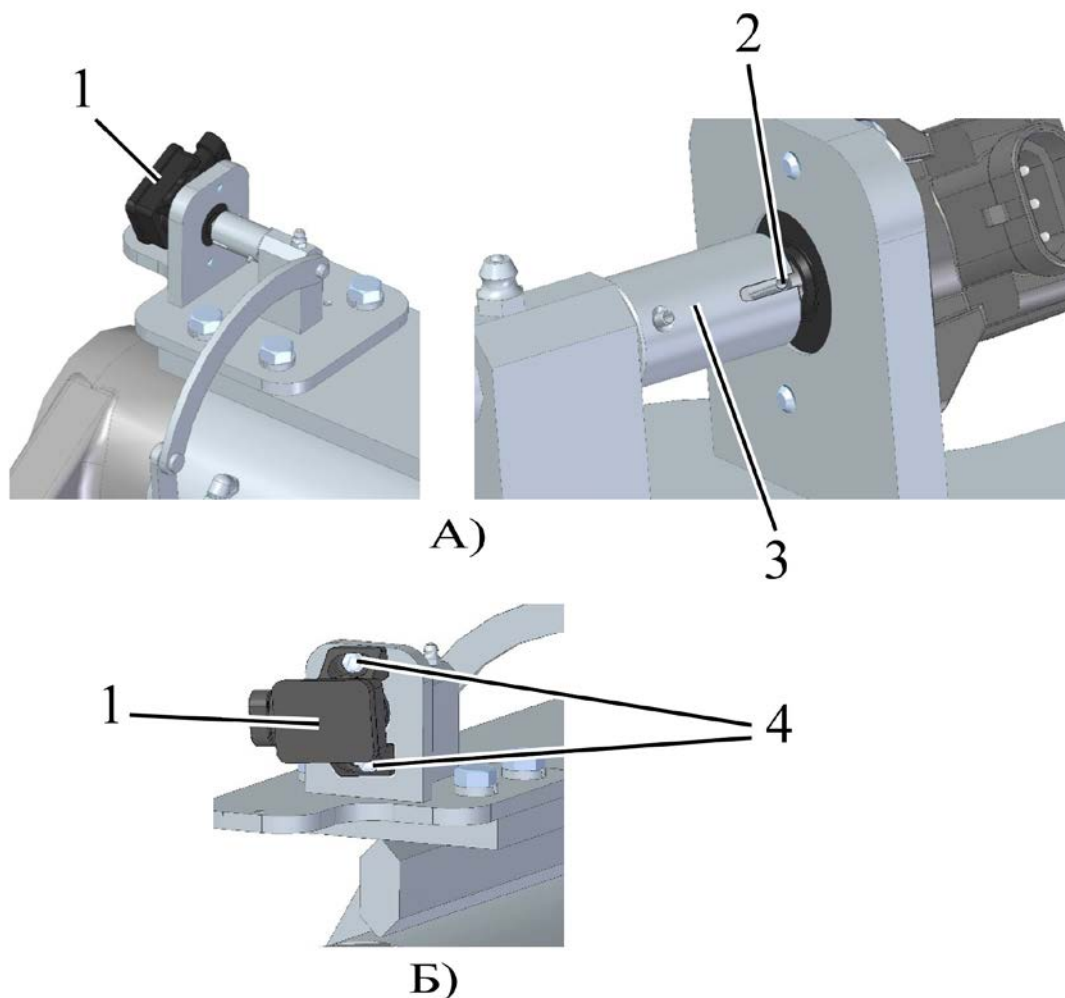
а – Установка пружинного штифта на вал позиционного датчика
